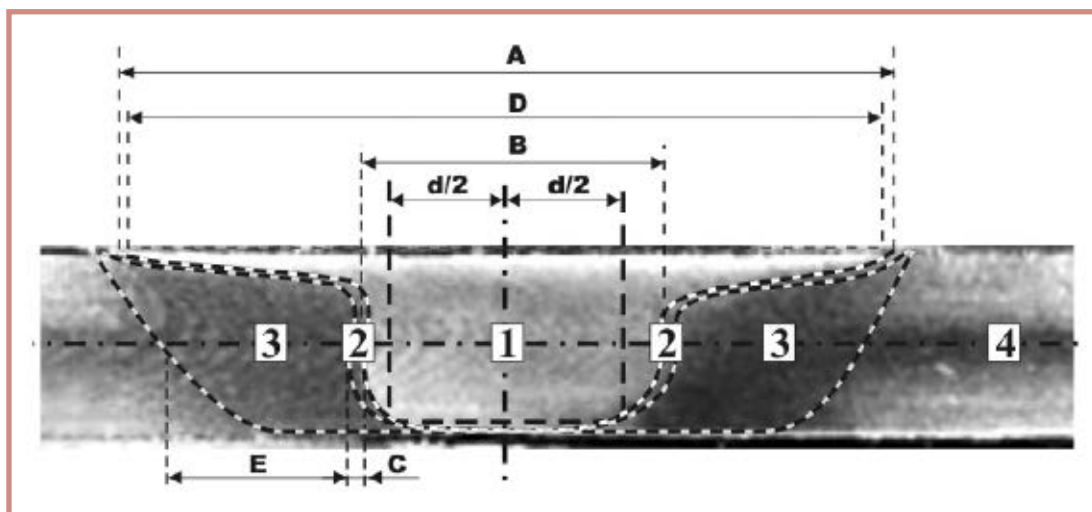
Макроструктура сварного соединения, выполненного сваркой трением с перемешиванием: 1 — сварной шов; 2 — зона термомеханического воздействия; 3 — зона термического влияния; 4 — основной металл
